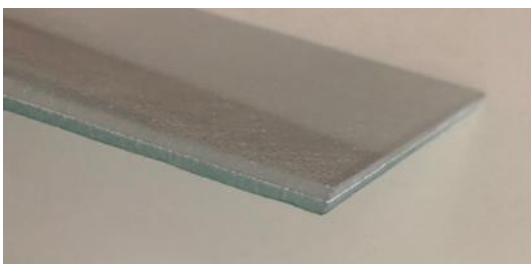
Beispiel für eine Waterjet-Schnittkante
